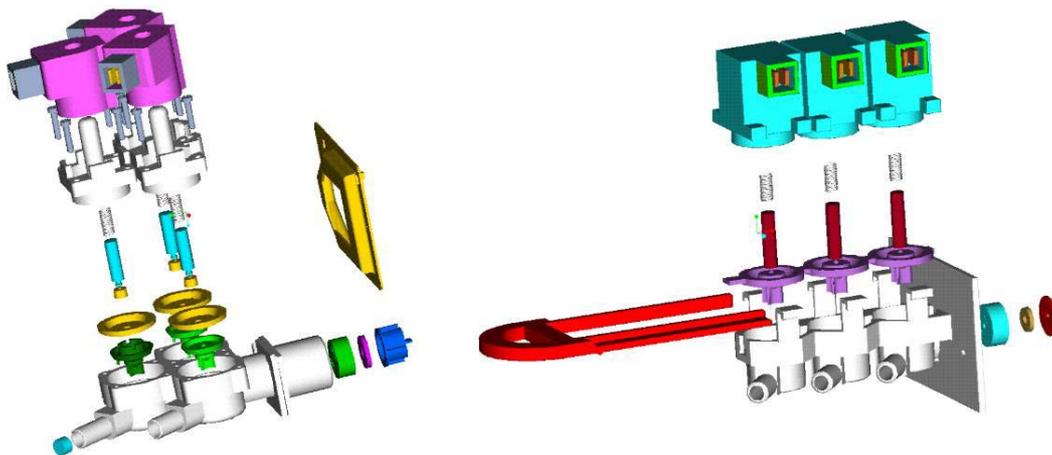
Explosionsdarstellungen der Ausgangs- (links) und demontagegerecht umgestalteten Ventilbaugruppe (rechts)
